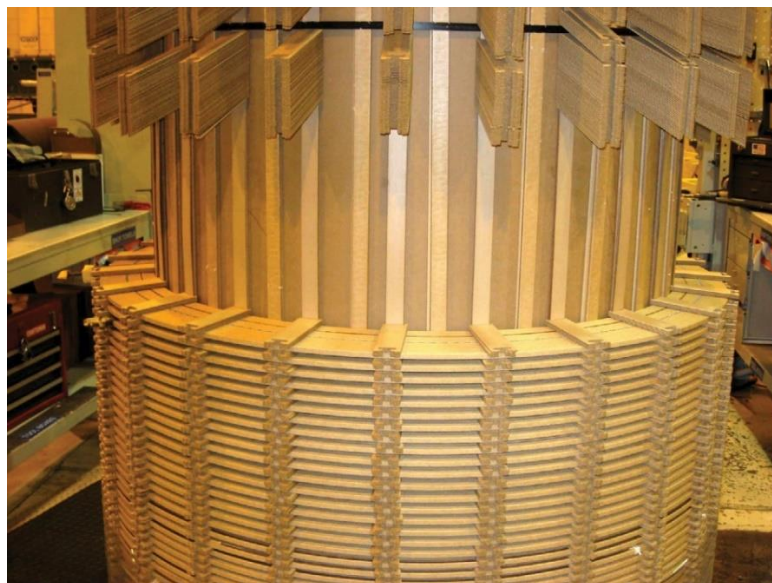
Construção do isolamento entre bobinas durante fabricação de um transformador.
